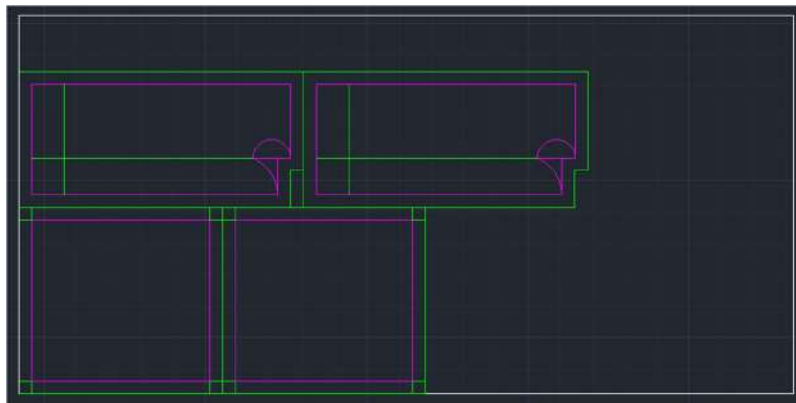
Patrones de corte de carbono para el flap y endplate de prueba
